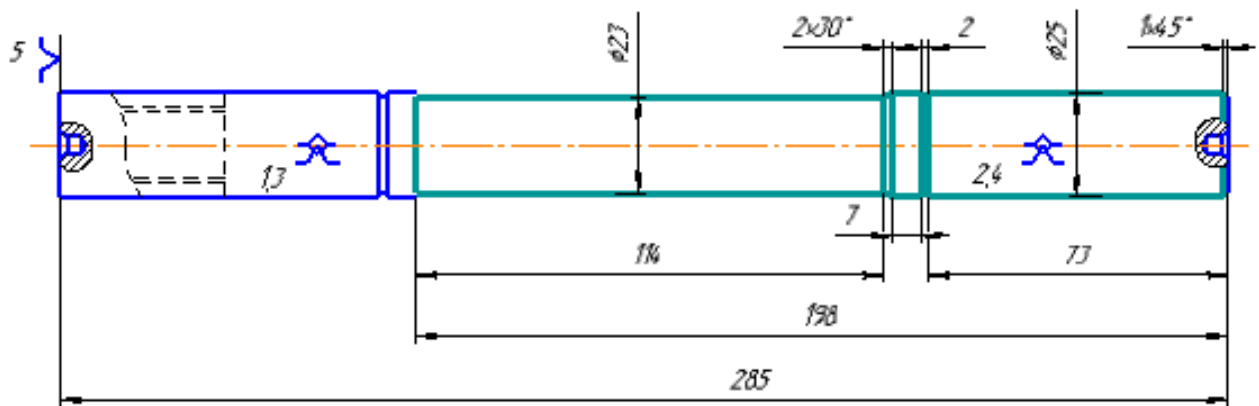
Обробка деталі при токарно-багаторіздевій операції.
